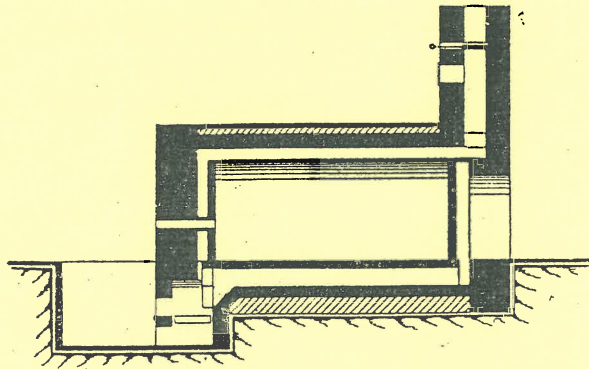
Muffelofen mit wagerechter Flammenführung. Längsschnitt.
